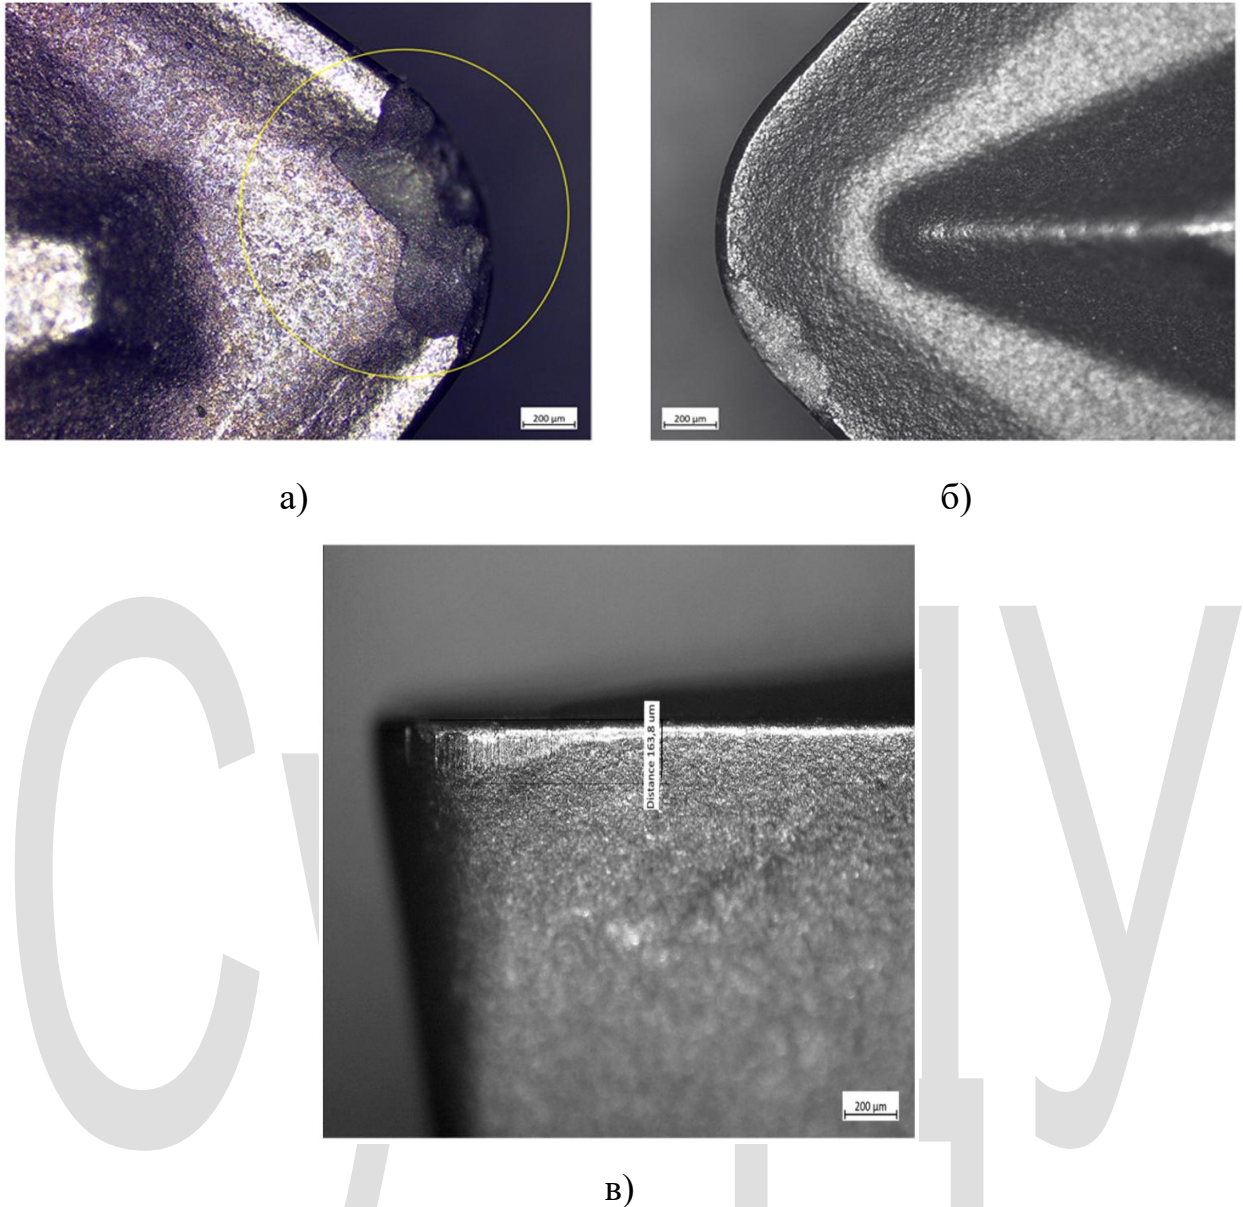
Вимірювання зносу поверхні ріжучої пластини за допомогою мікроскопа Carl Zeiss Primotech D/A ESD: а) зовнішня поверхня інструменту, б) лицьова частини пошкодження інструменту, в) вимірний знос бокової сторони 163,8 мкм.
